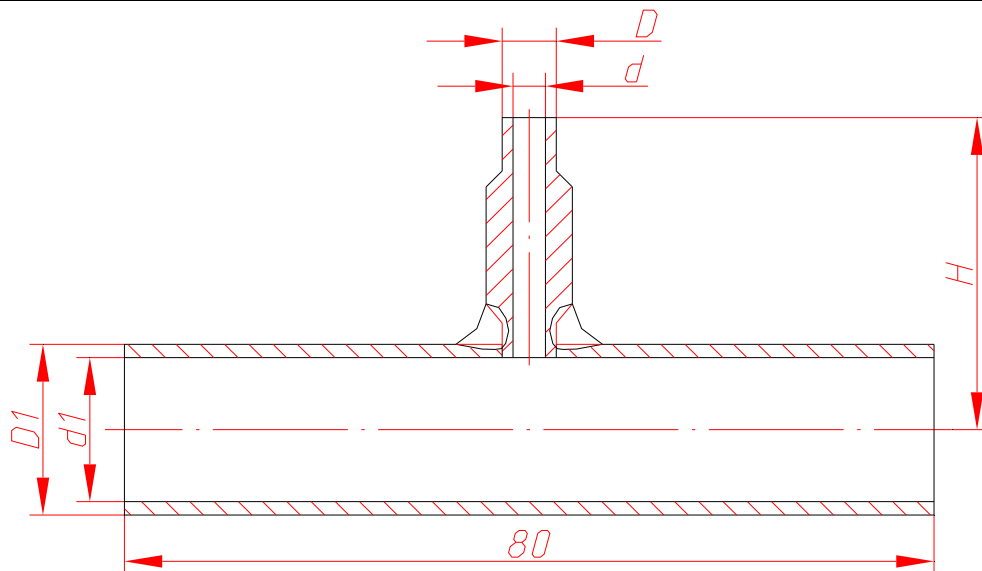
Тройник сварной типа ...-ТС-... Общий вид.
